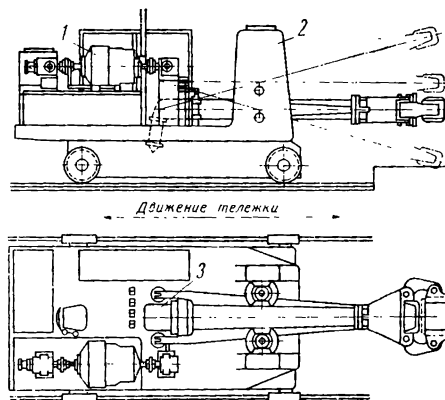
Схема тележного узкоколейного манипулятора (III типа): 1 — механизм подъема хобота; 2 — механизм подъема хобота; 3 — механизм поворота хобота
